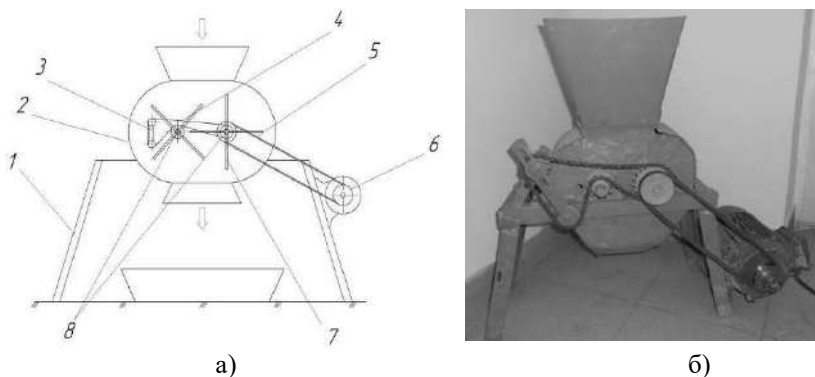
Пристрій для подрібнення промороженого сапропелю: а) схема пристрою для подрібнення: 1 – корпус; 2 – кожух; 3 – натяжний пристрій; 4 – ланцюгова передача; 5 – пасова передача; 6 – двигун; 7 – лопаті; 8 – ротор; б) фото пристрою для подрібнення промороженого сапропелю
